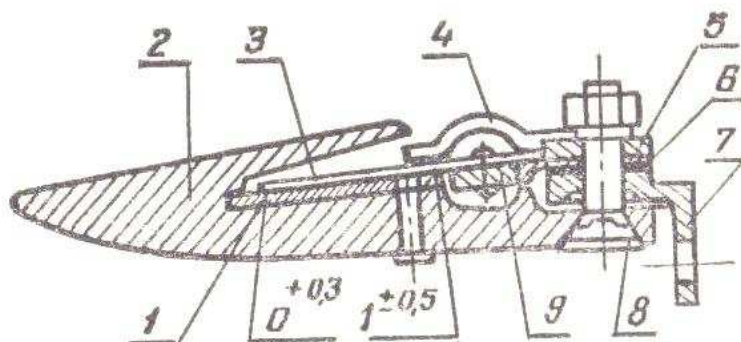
Режущий аппарат комбайна СК-6: 1 – вкладыш; 2 – палец; 3 – сегмент ножа; 4 – прижим ножа; 5 – пластина трения; 6 – регулировочная шайба; 7 – пальцевый брус; 8 – болт; 9 – спинка ножа
